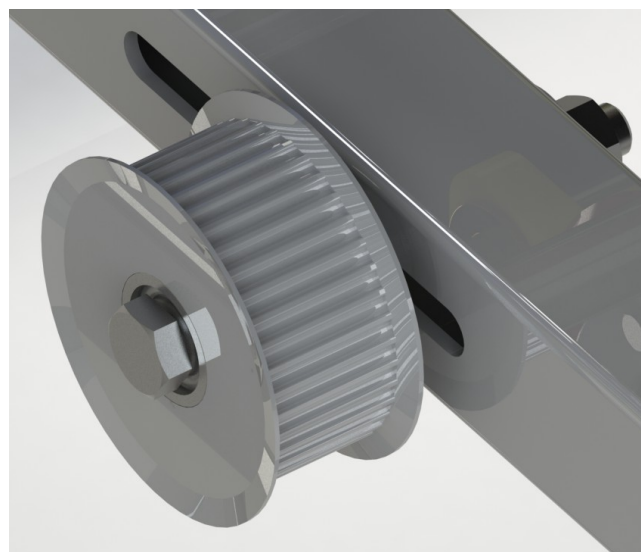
Uložení hnané řemenice v elmag. spojkách
